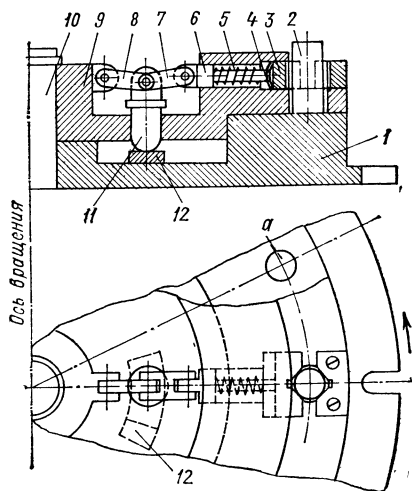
Схема автоматизации закрепления и раскрепления деталей при непрерывном фрезеровании
